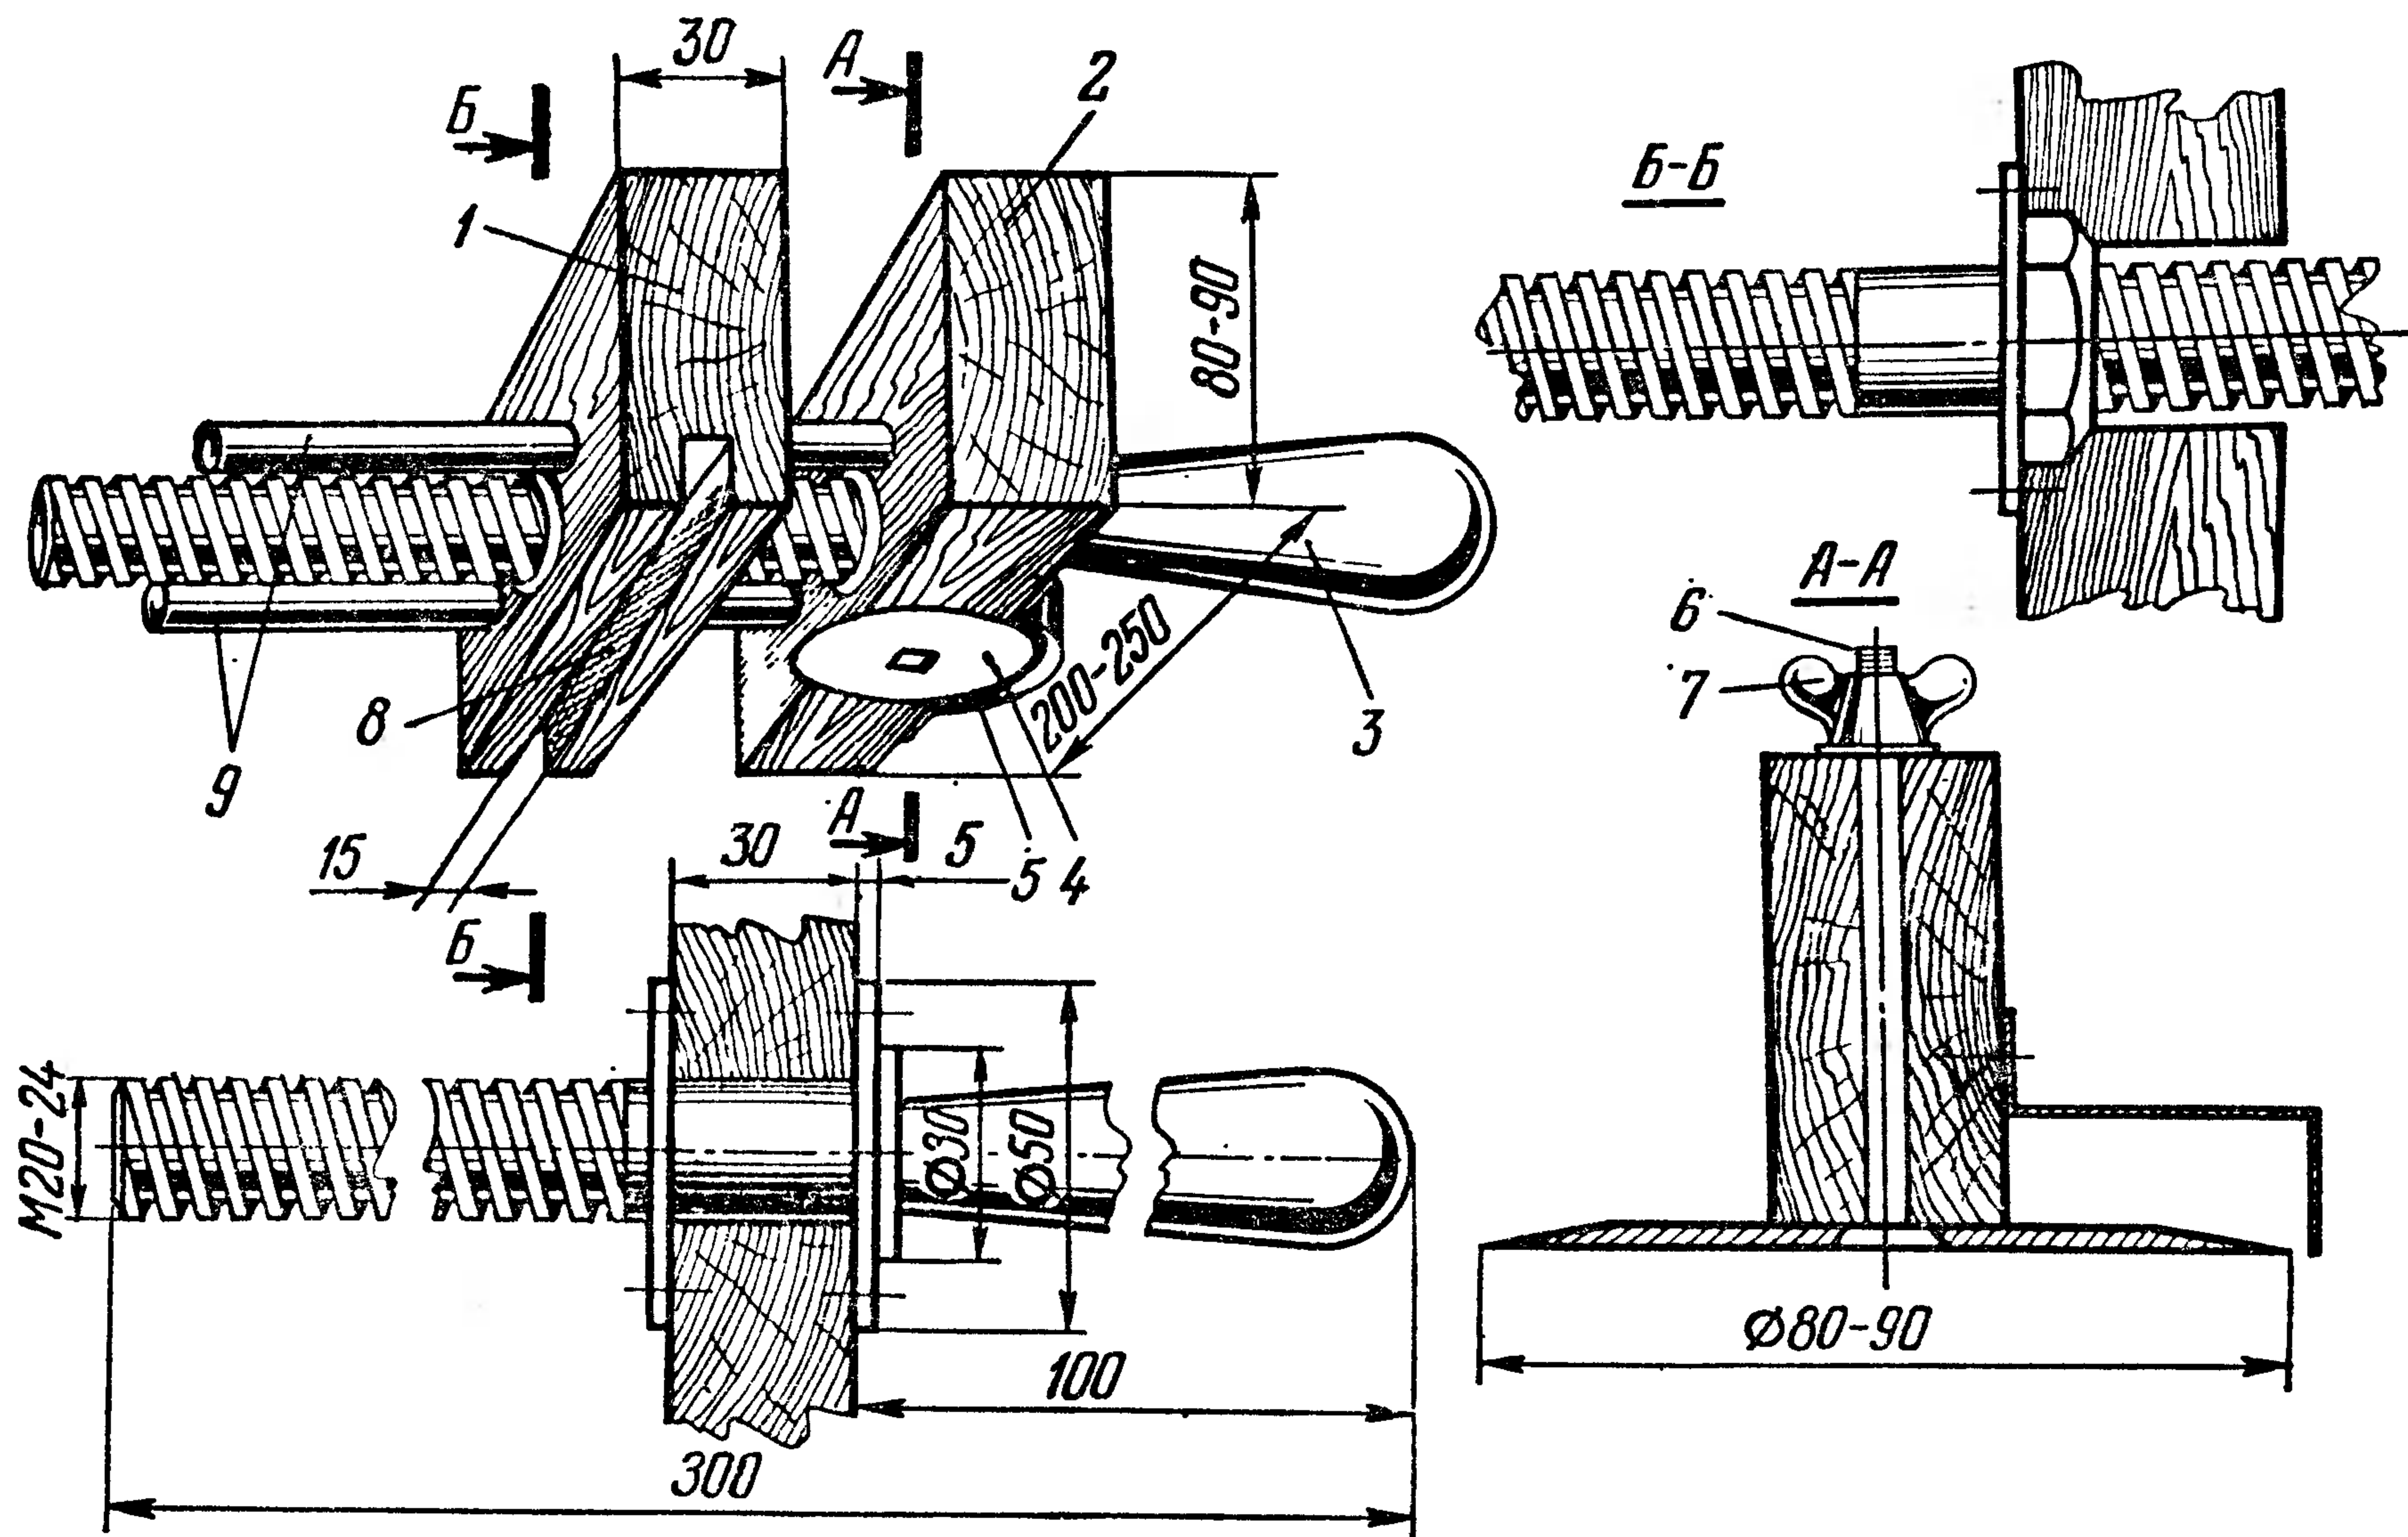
Гобель: 1 — подвижная планка; 2 — неподвижная планка; 3 — поджимной винт с рукояткой; 4 — дисковый нож; 5 — ограждение дискового ножа; 6 — фиксирующий винт дискового ножа; 7 — гайка; 8 — паз для направляющего полоза переплетных тисков; 9 — направляющие стержни.
